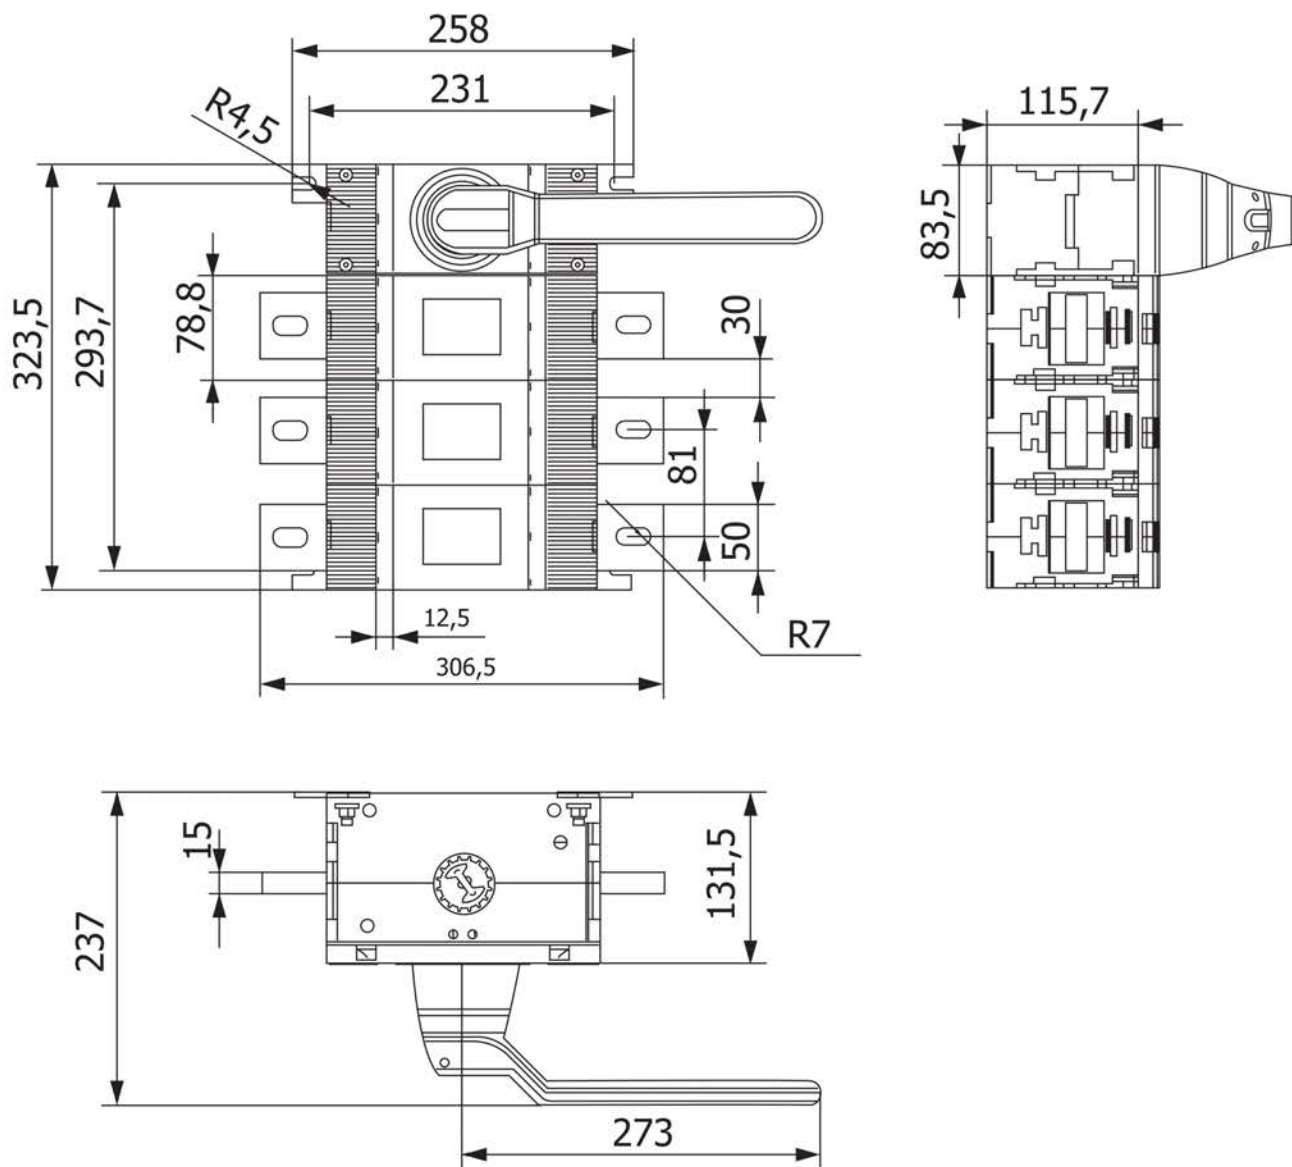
Габаритные и установочные размеры рубильников 1000-1600А
